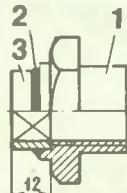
Переделанный храповик ВАЗ—2105: 1 — храповик; 2 — сварочный шов; 3 — отрезок торцевой головки.
